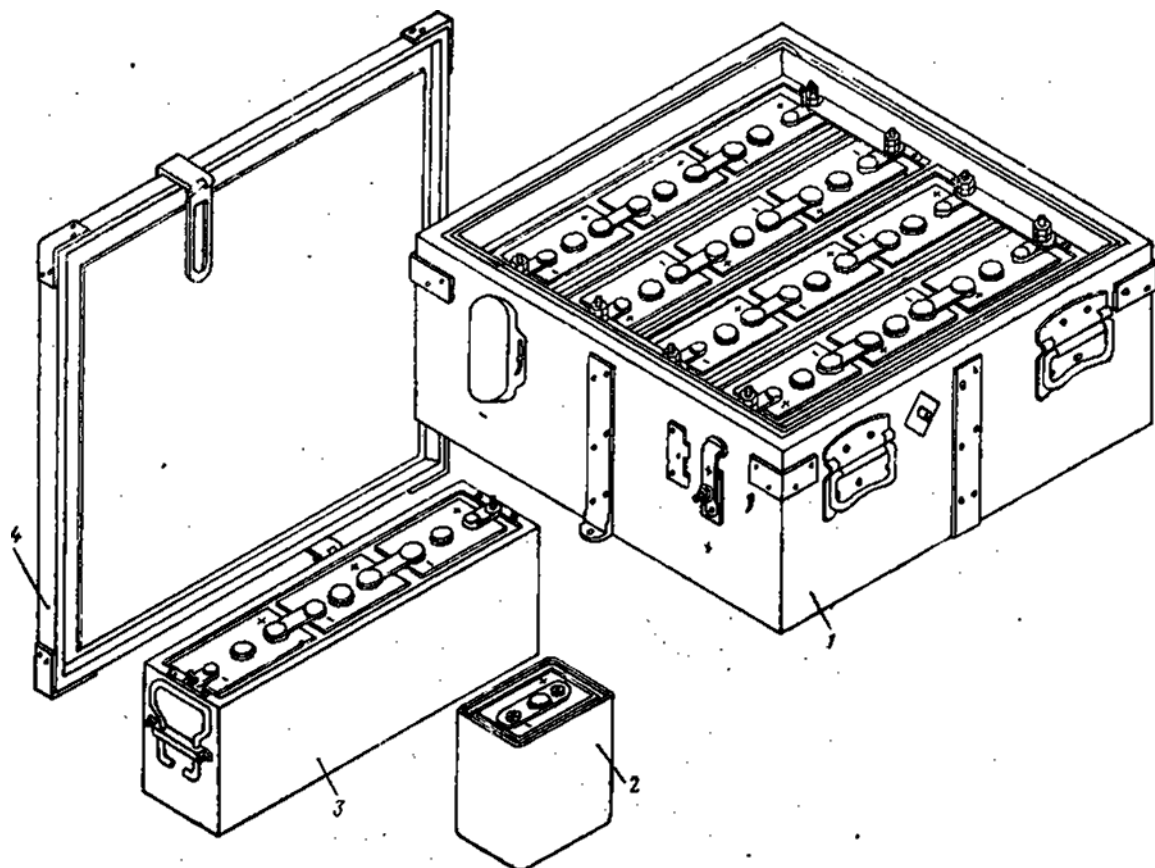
Габаритный чертеж батарей типа 12-A-30, 12-CAM-28, 12-ACAM-23 и полубатареи типа 12-CAM-55.
